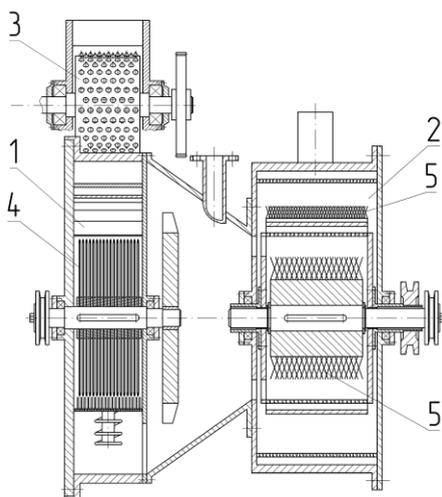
Роторно-центробежный агрегат комбинированного действия: 1, 2 – камеры измельчения; 3 – шипованные валки; 4 – дисковые фрезы; 5 – иглофрезерные рабочие органы
